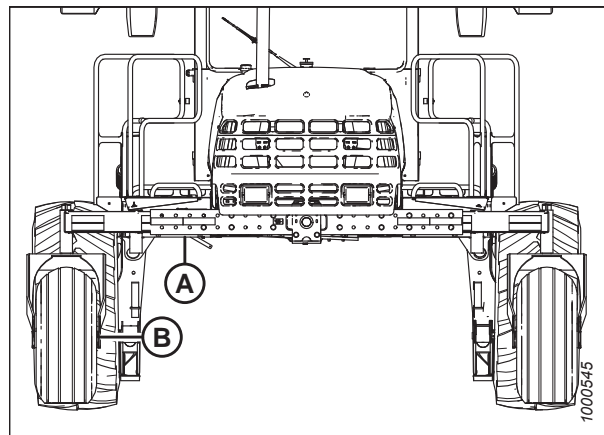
Опорные колеса и балансир (вид в положении двигателем вперед)
